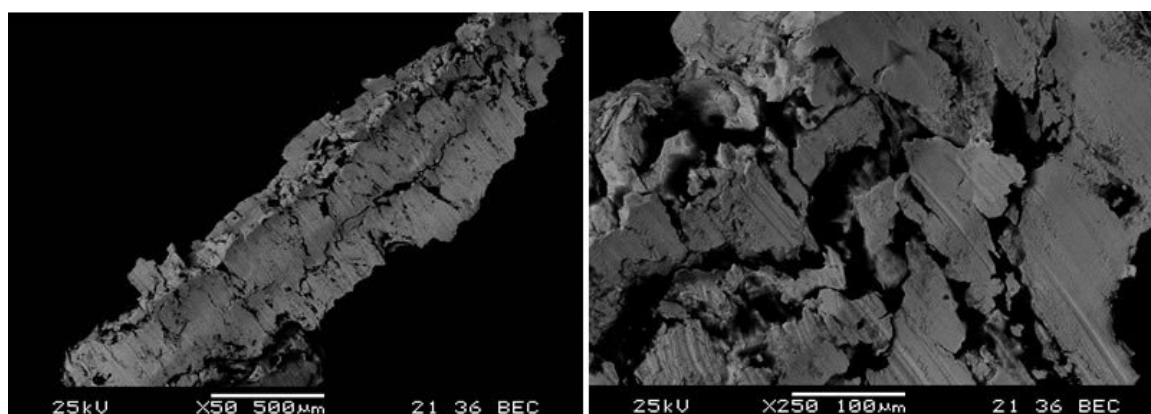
Aspecto do cavaco (a) e da superfície inferior do cavaco (b) produzido na usinagem do ferro fundido cinzento a 600 m/min.
